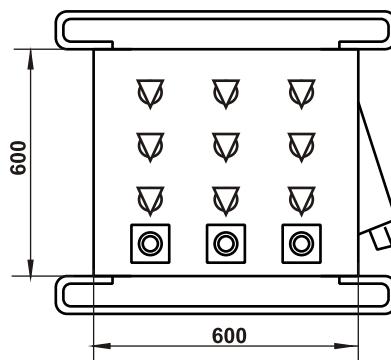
Вид в разрезе шкафа ШПТ (вид А для Рис. 1)
